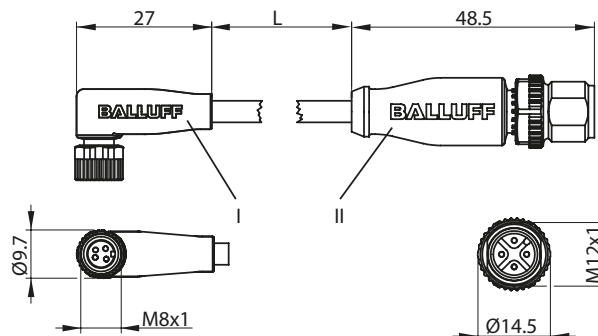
Connecteur femelle coudé – connecteur mâle droit
